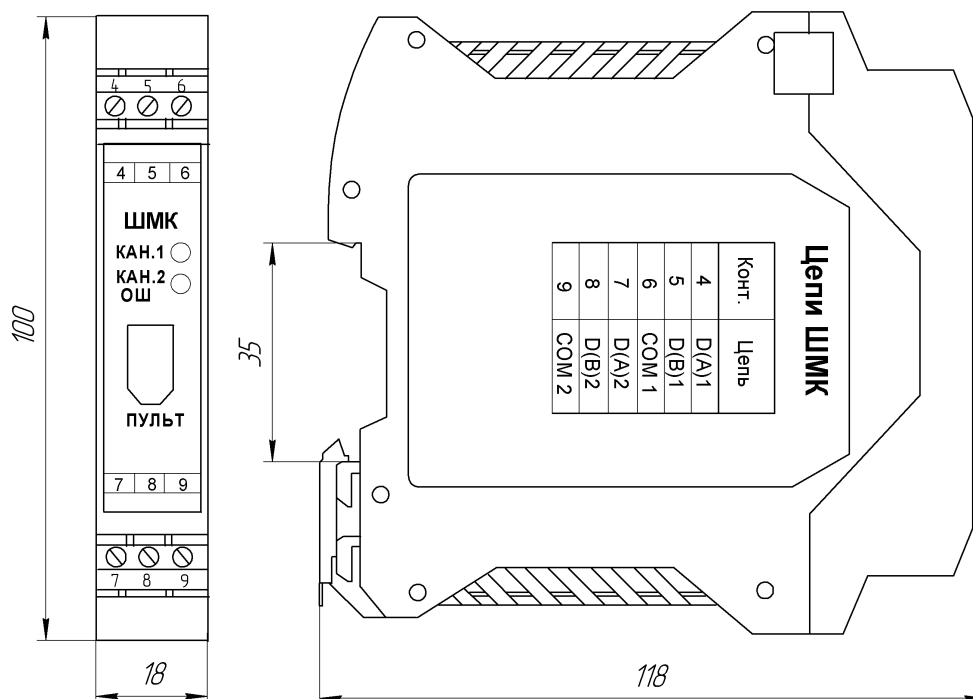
, а – Внешний вид и габаритные размеры микроконтроллера ШМК
